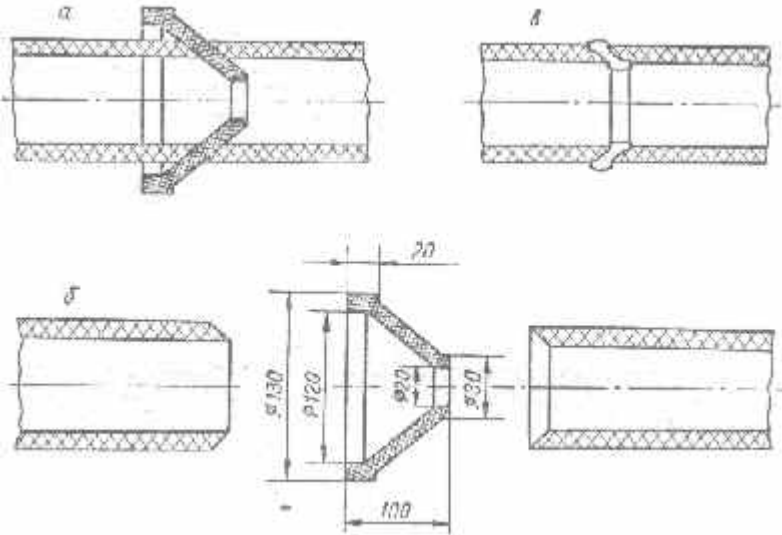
Последовательность процесса раструбно-стыковой сварки:
